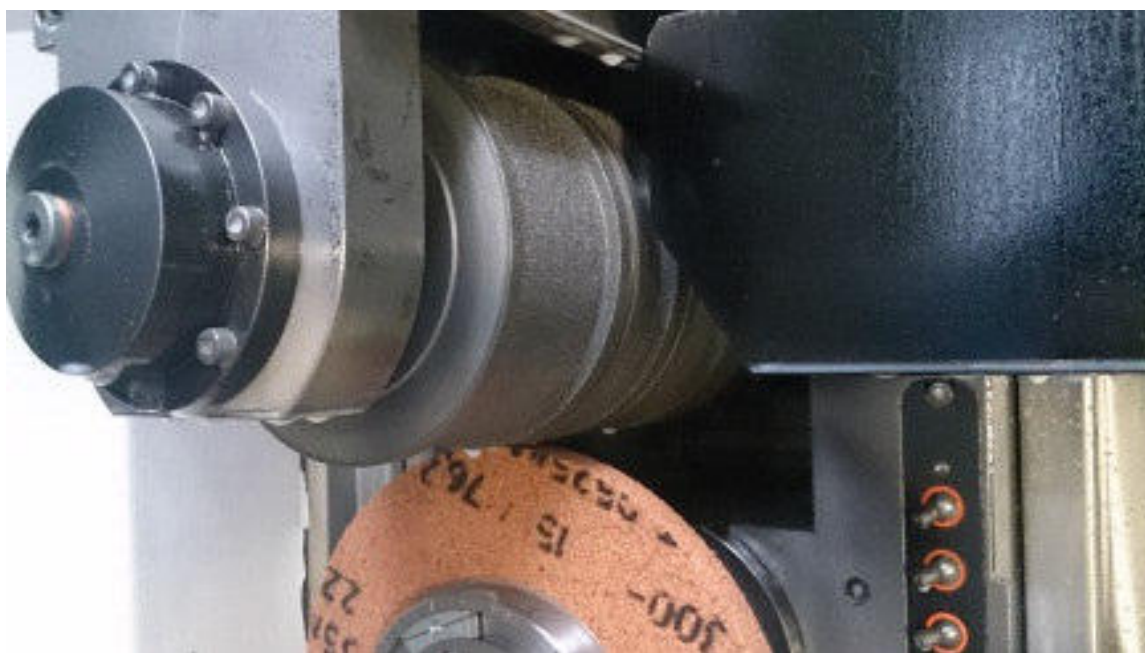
Устройство непрерывной правки шлифовального круга
